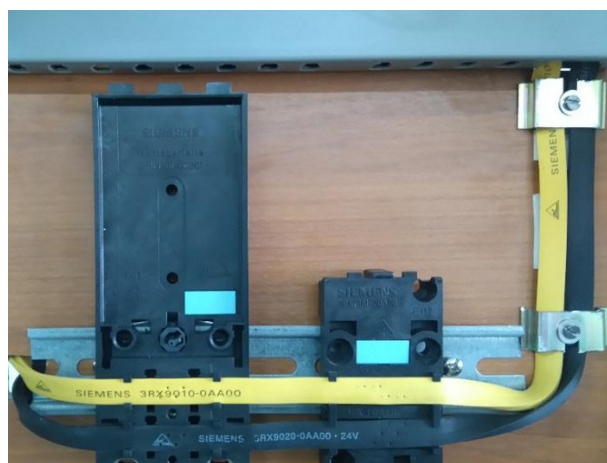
Instalación de las cajas de montaje en conjunto con el cable
